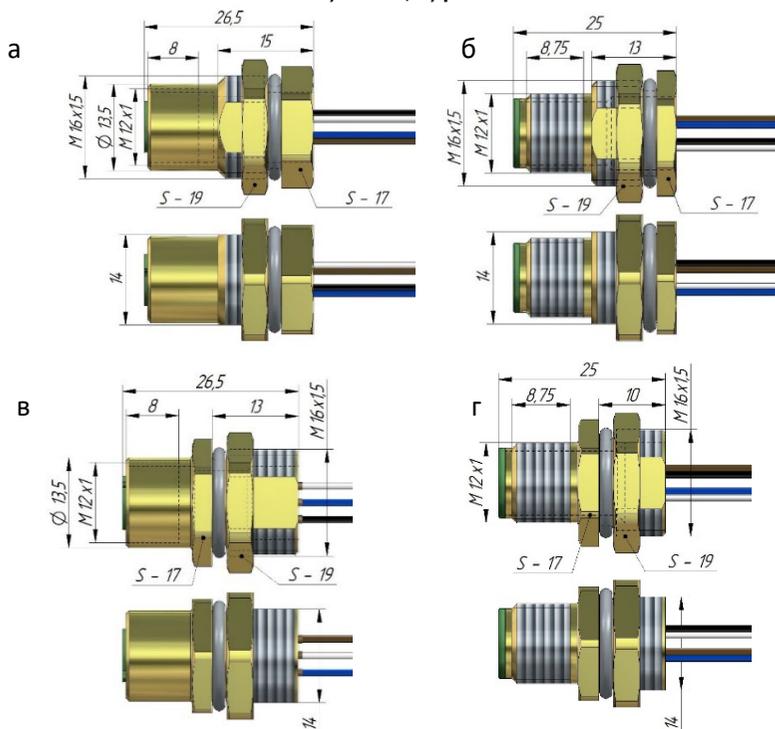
Внешний вид и габаритные размеры блочных разъемов:
